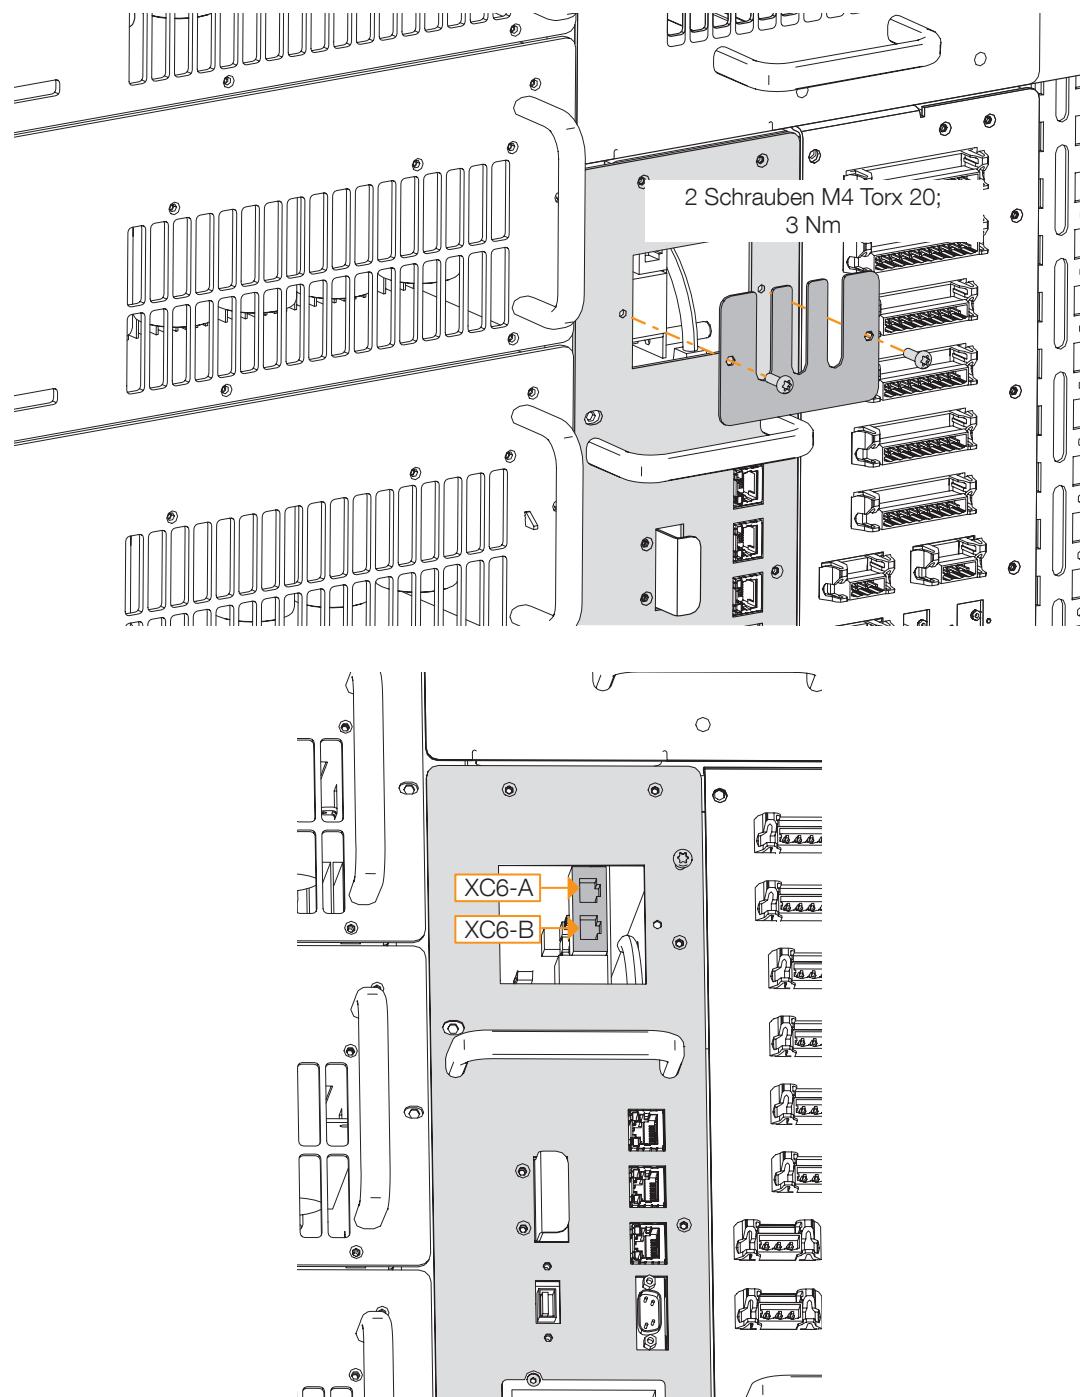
Einbauort der RJ-Kabel für die Parallelschaltung von C-Cab Master und Extension
